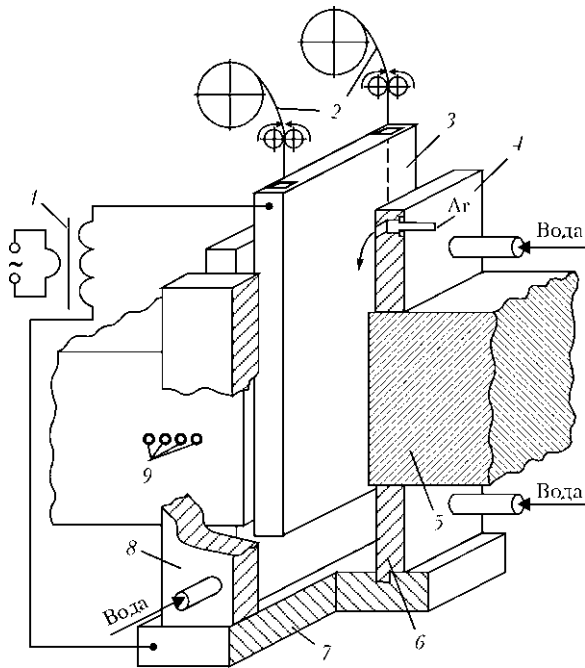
Схема сборки образцов под ЭШС: 1 — источник питания; 2 — сварочная проволока; 3 — плавящийся мундштук; 4 — выводная водоохлаждаемая формирующая планка; 5 — свариваемый образец; 6 — входная водоохлаждаемая формирующая планка; 7 — поддон; 8 — боковое формирующее устройство; 9 — отверстия для термопар
